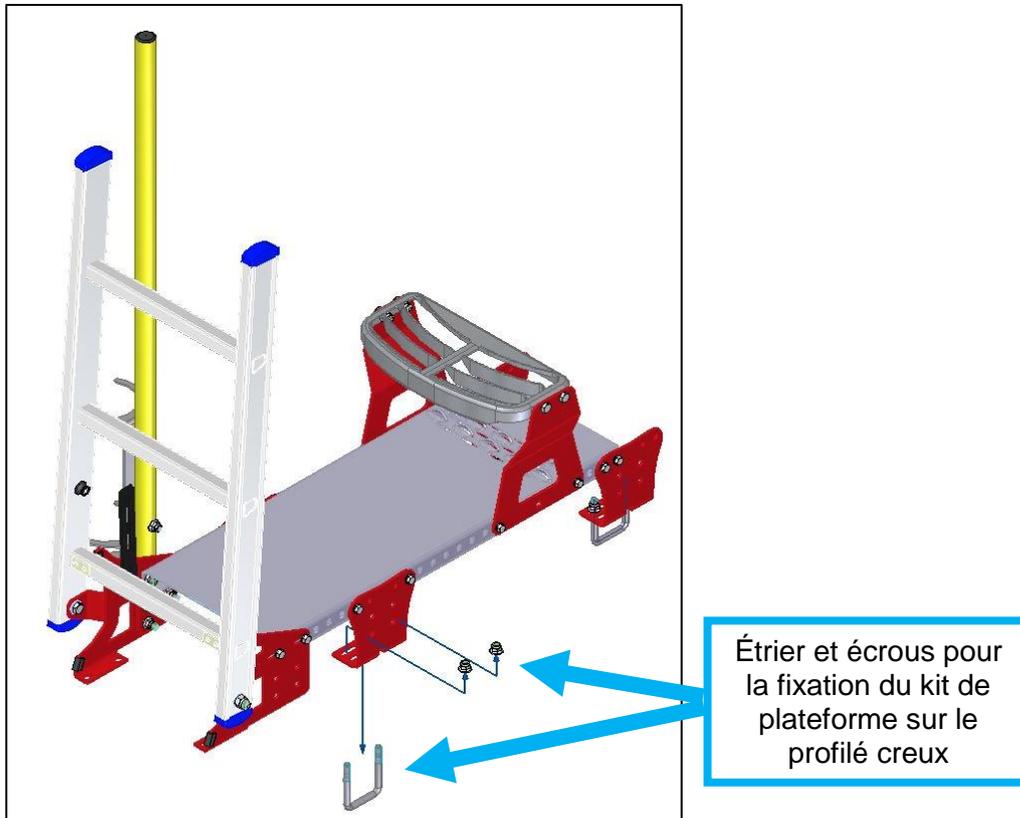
composants du kit de plateforme VS600-1200 sans roue de jauge à l'arrière
